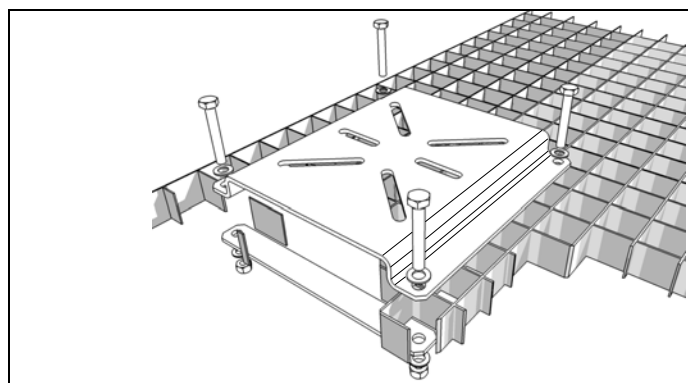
Montage de la plaque de montage pour étau d'établi
